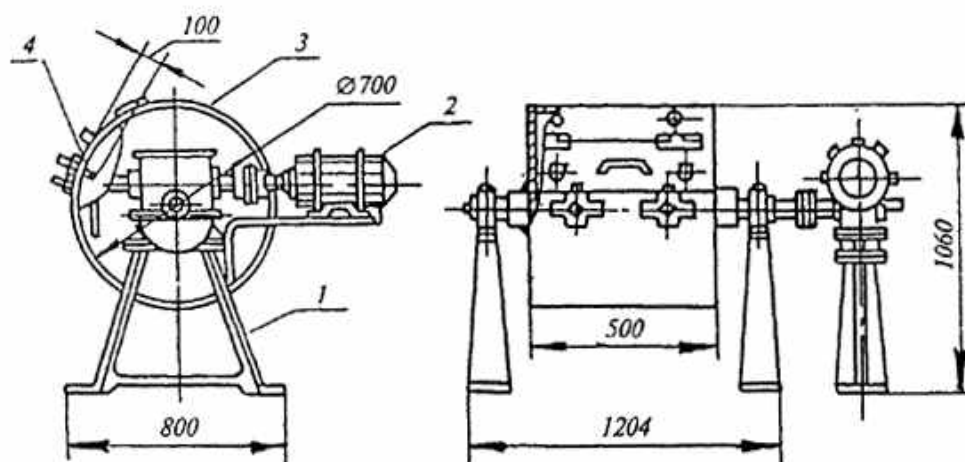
Полочный барабан: 1 – станина; 2 – двигатель; 3 – барабан; 4 – полка барабана
